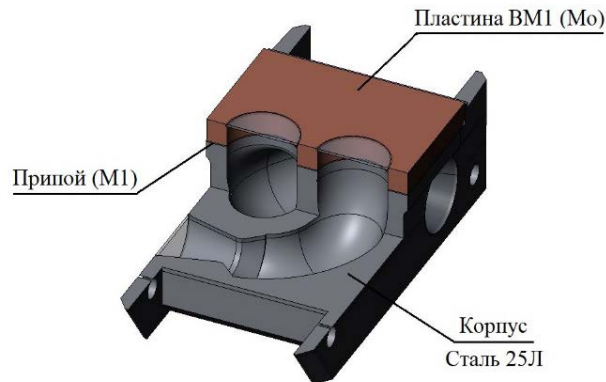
Конструкция детали «Корпус» в разрезе
